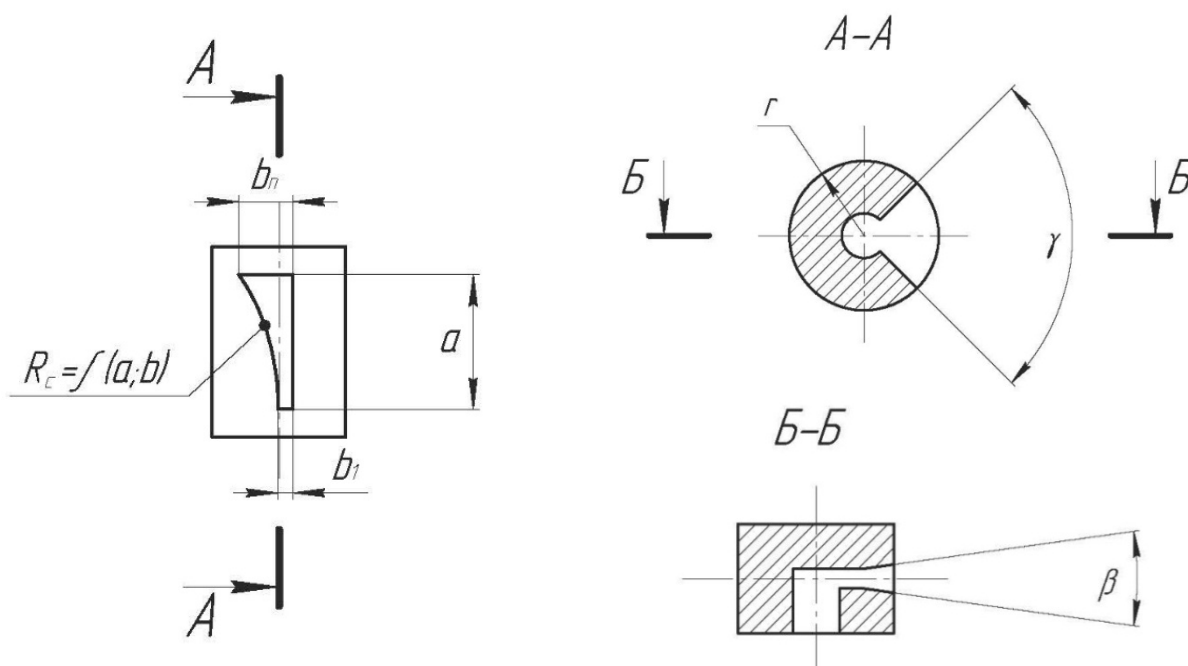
Схема сопла веерной дождевальной насадки
